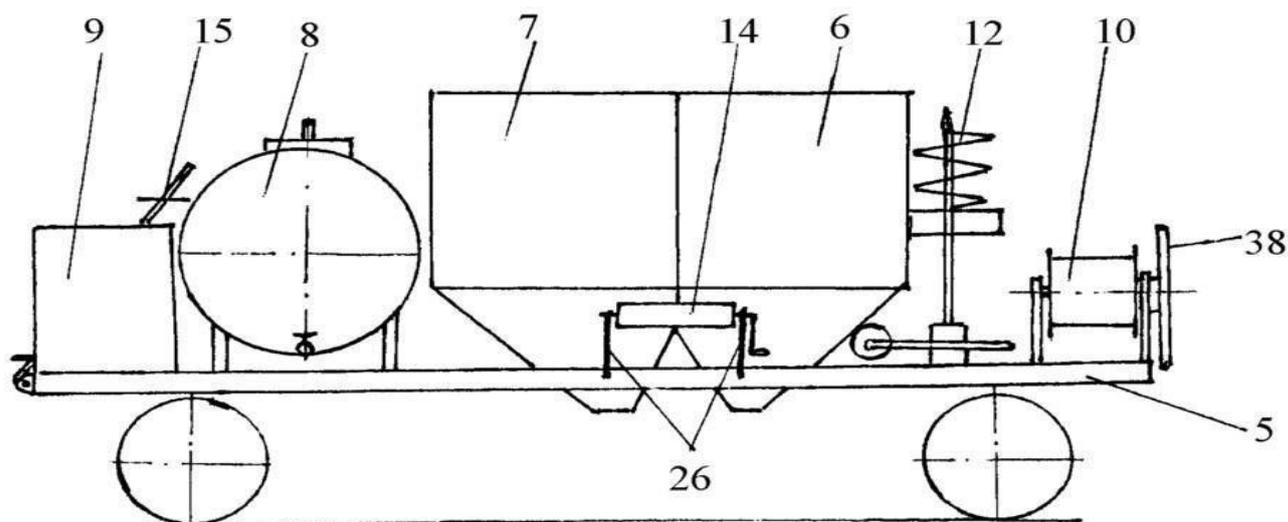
Лесопосадочный агрегат (вид сбоку)
